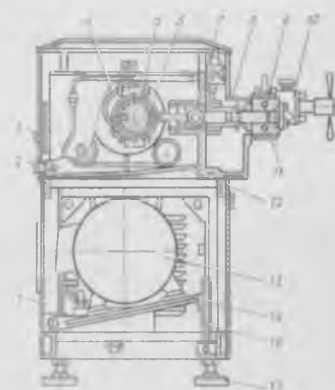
Гомогенизатор А1-ОГМ: 1 — станция; 2 — сливная пробка; 3 — маслоуказатель; 4 — кривошипно-шатунный механизм; 5 — шатуны; 6 — вкладыш; 7 — палец; 8 — ползуны; 9 — плунжер; 10 — гомогенизирующая головка; 11 — плунжерный блок; 12 — шмеевик; 13 — электродвигатель; 14 — плита; 15 — устройство для натяжения ремней; 16 — опора
